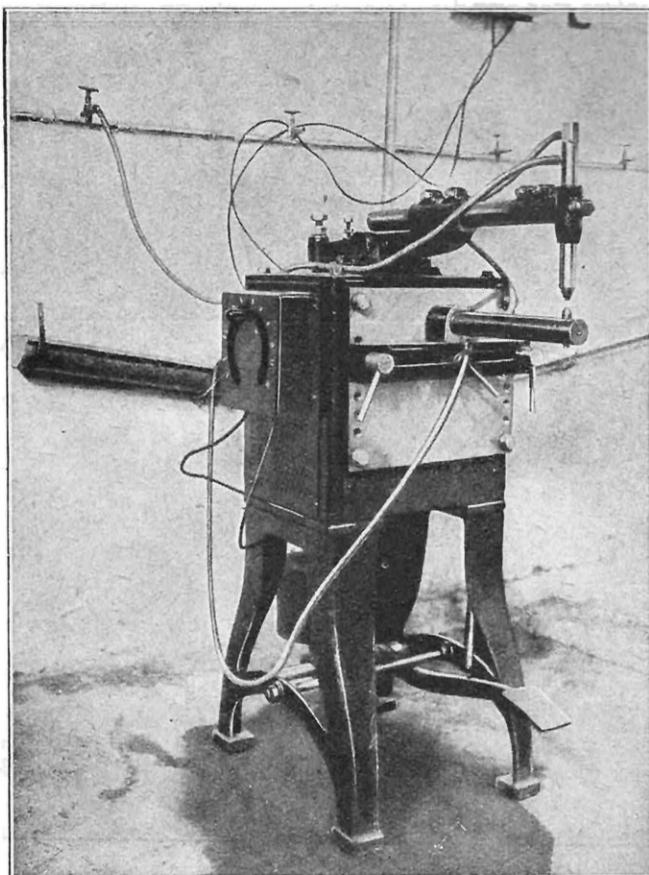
MACHINE CONSTRUITE POUR SOUDER ÉLECTRIQUEMENT PAR POINTS
